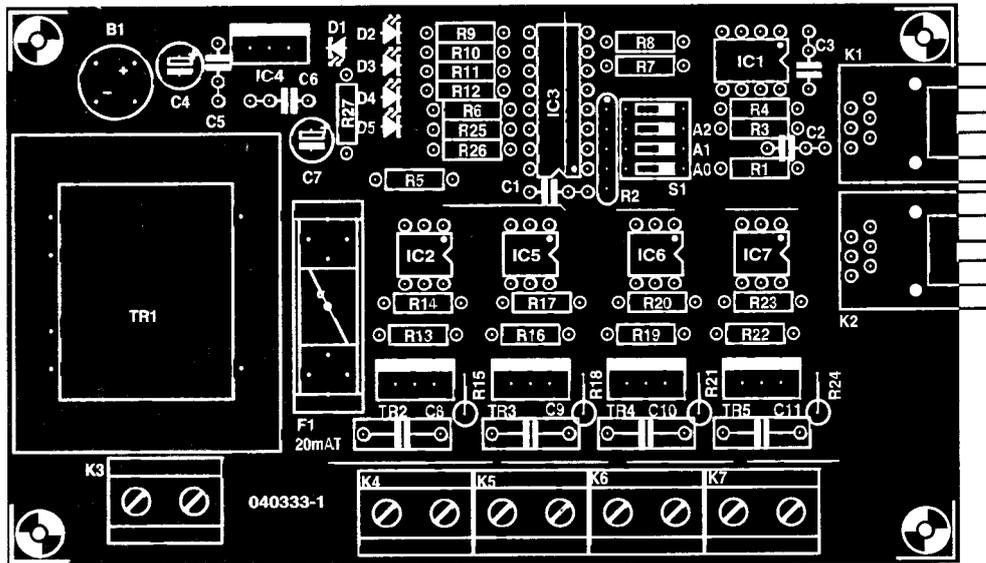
Mit dieser Platine ist das I²C-Fernschaltmodul schnell aufgebaut.
